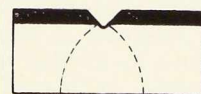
(ci-dessous). Aspect des soudures terminées.
